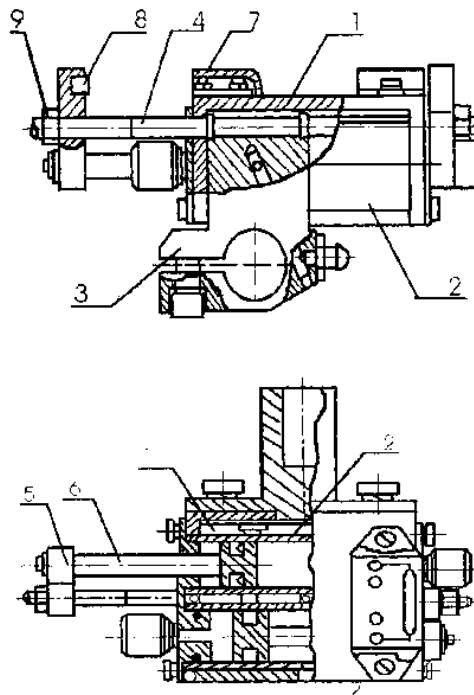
Модуль зсуву схвата: 1 – корпус; 2 – циліндр; 3 – каретка; 4 – шток;
